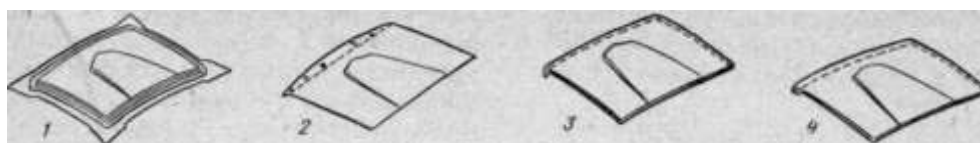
Последовательность процесса штамповки верхней панели капота ГАЗ: 1 — вытяжка; 2— обрезка по контуру и пробивка отверстий; 3—формование передней стороны и отбортовка фланцев задней и боковых сторон; 4— отбортовка передней стороны панели
